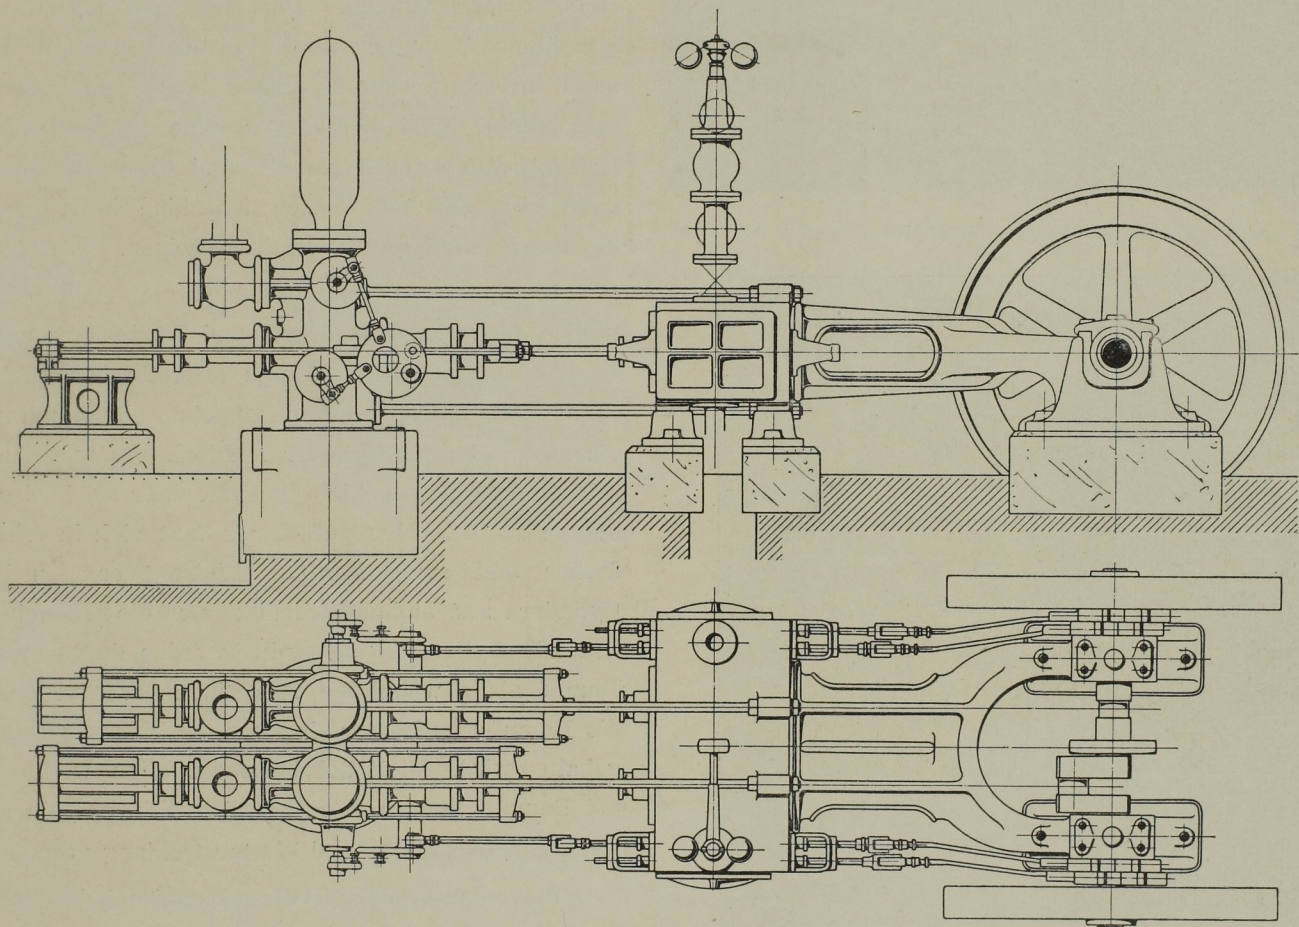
Seitenansicht und Grundriss. Massst. 1:32.
